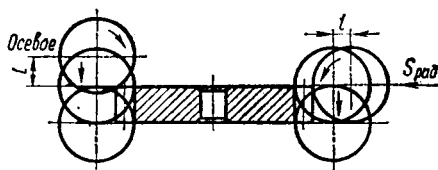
Схема зубофрезерования с радиальным врезанием фрезы
